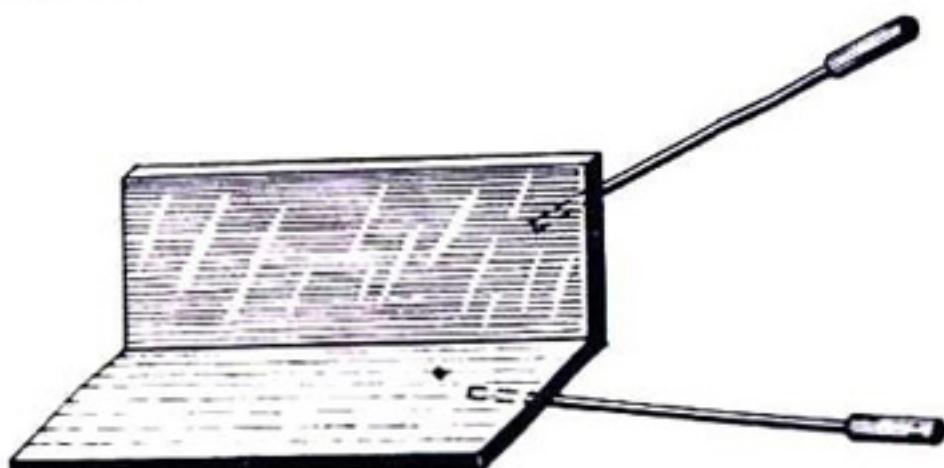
Уголок для сварки дренажной арматуры.
